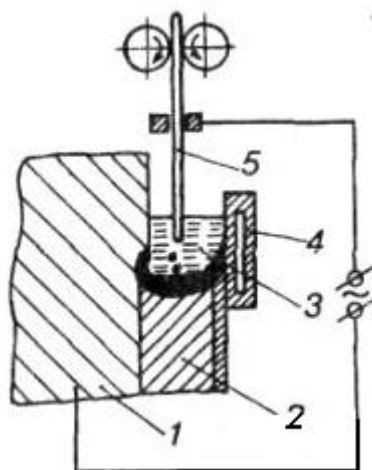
Схема электрошлаковой наплавки на вертикальную поверхность: 1 — изделие; 2 — наплавленный слой; 3 — шлак; 4 — кристаллизатор; 5 — электродная проволока
